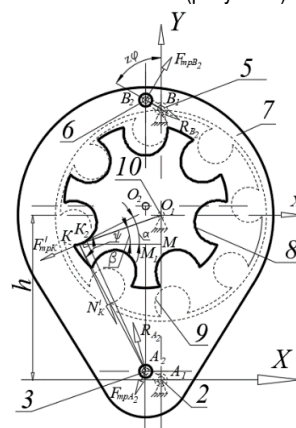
Схема действия сил на зубчатый венец 8 с сателлитом 7 эксцентриковой передачи с параллельным расположением входного и выходного валов
